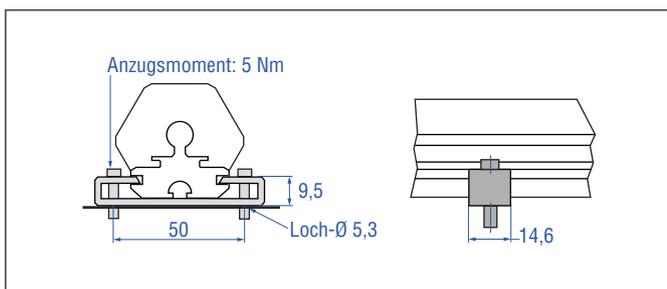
Montageklammern (Artikelnr. 400 802) mit Zylinderschraube M5×20
